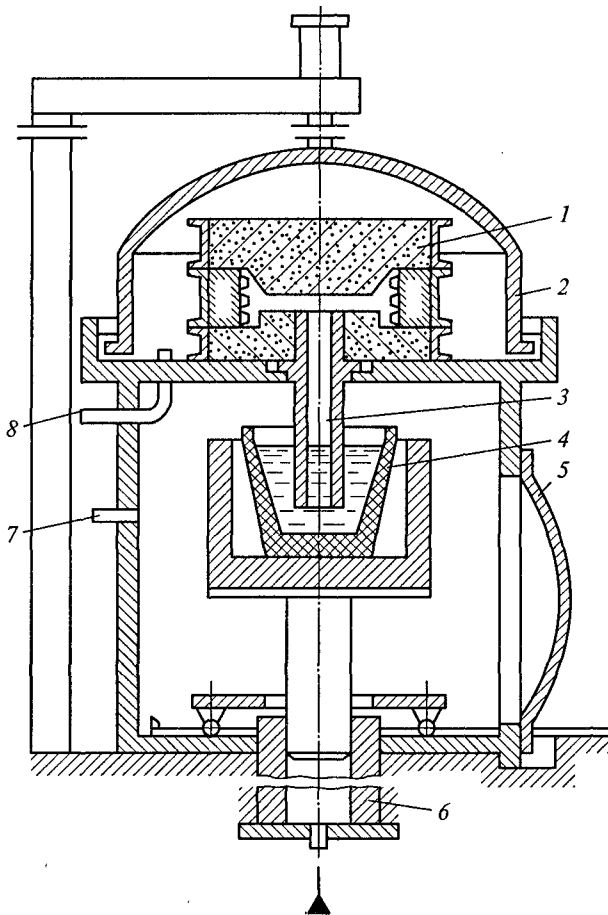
Схема установки для вакуумно-компрессорного литья:
